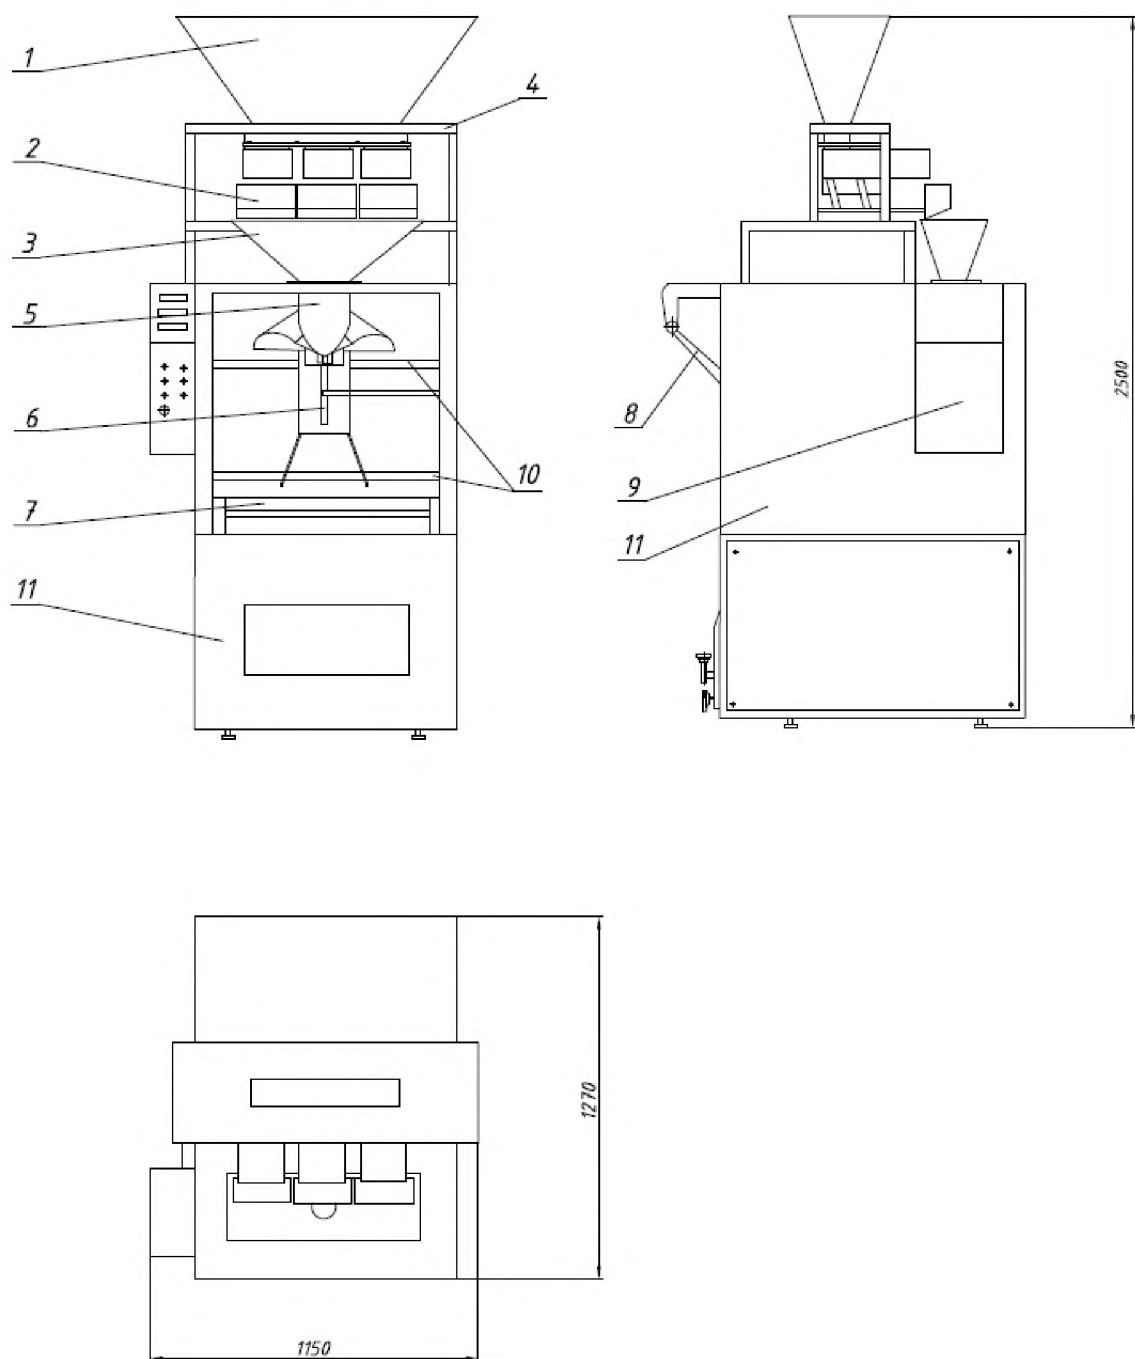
Автомат фасувально-пакувальний УФС-30А-3В: 1 – бункер завантажувальний; 2 – дозатор ваговий; 3 – бункер приймальний; 4 – станина; 5 – рукавотворювач; 6 – механізм поздовжнього зварювання; 7 – механізм поперечного зварювання, протягування і відрізання; 8 – механізм подачі плівки; 9 – блок керування; 10 – рама; 11 – захисний кожух
